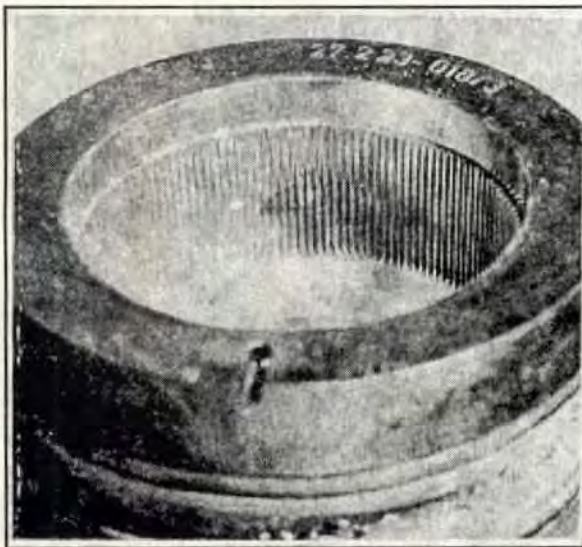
Corrosión del molde por inclusión de aire (efecto Diesel)
